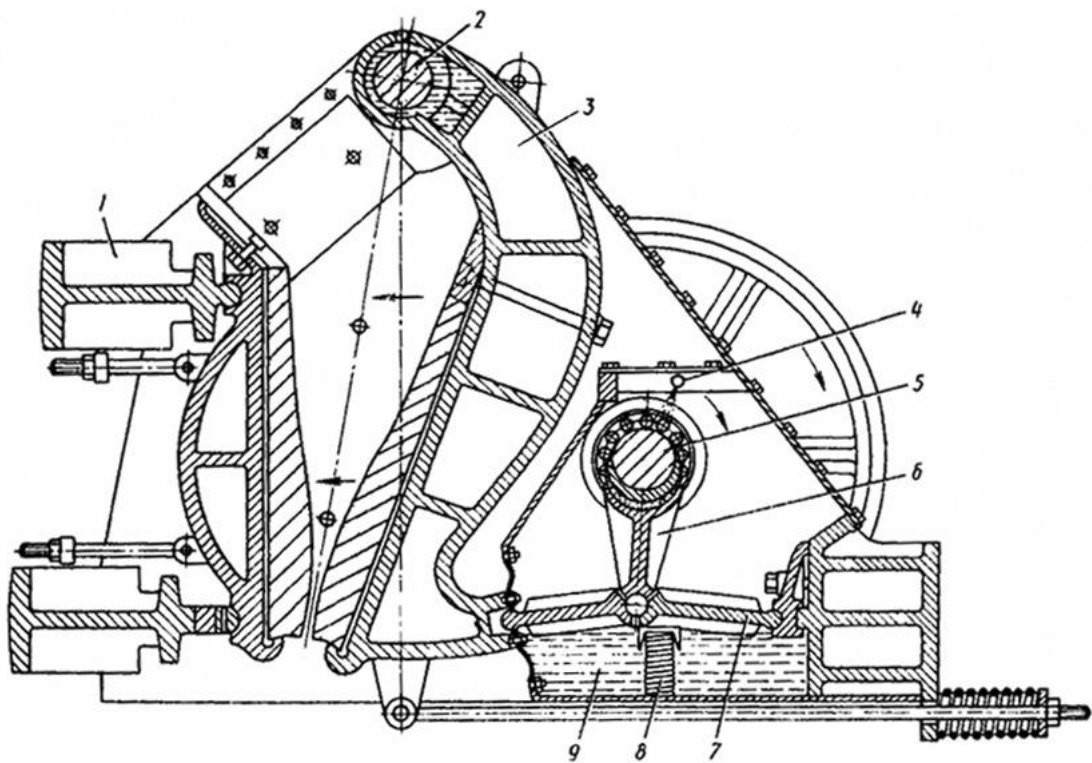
Щокова дробарка «Кью-Кен»:
